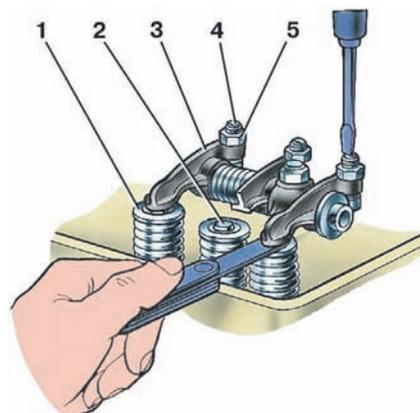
Регулювання зазору між коромислом і клапаном: 1 – тарілка пружини; 2 – клапан; 3 – коромисло; 4 – регульовальний гвинт; 5 – контргайка
